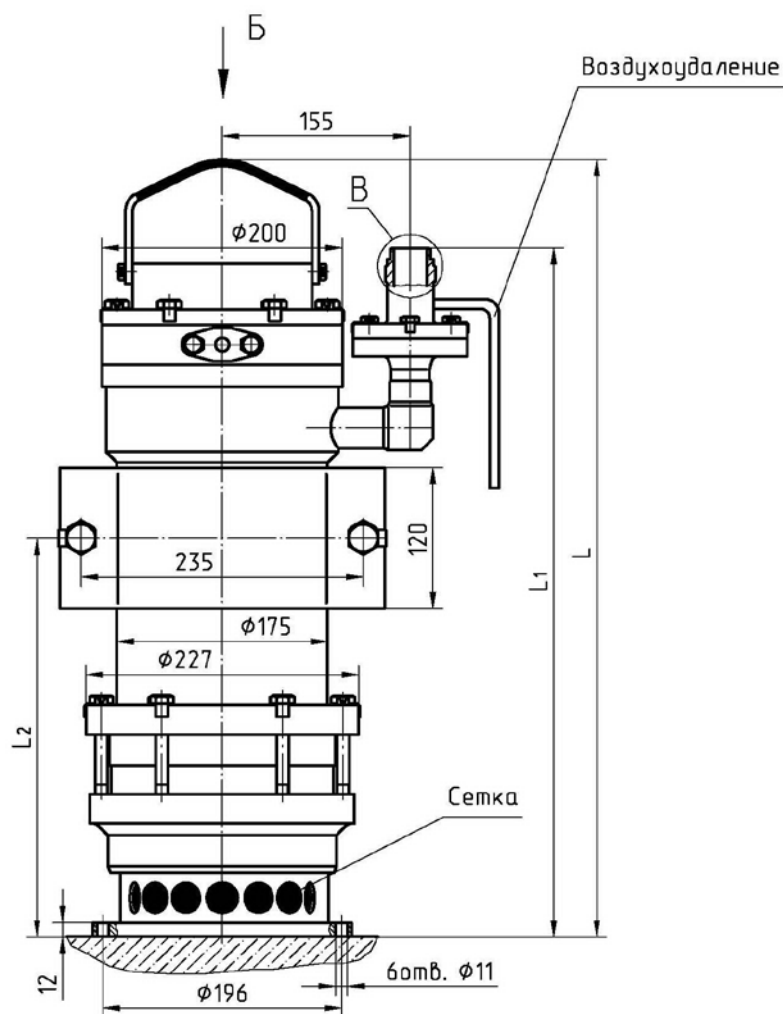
Габаритный чертеж насосного агрегата типа ЦНА 65/90
